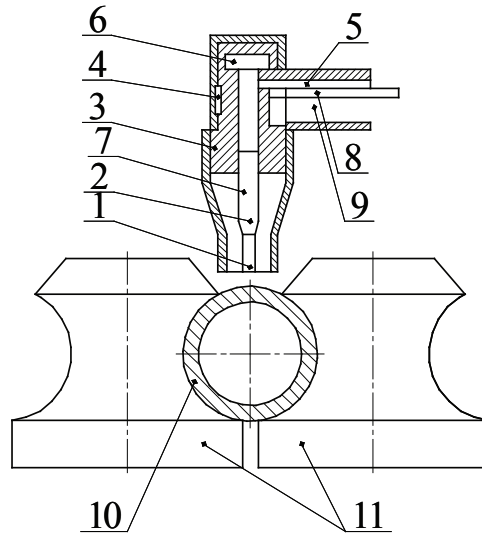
Схема аргано-дуговой сварки труб:
